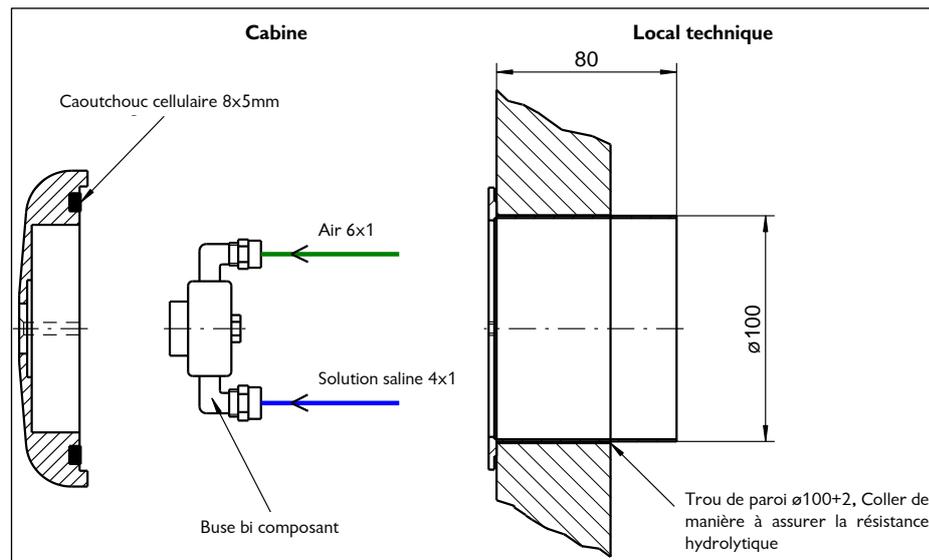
, plan de montage du passe-paroi avec capuchon de buse
